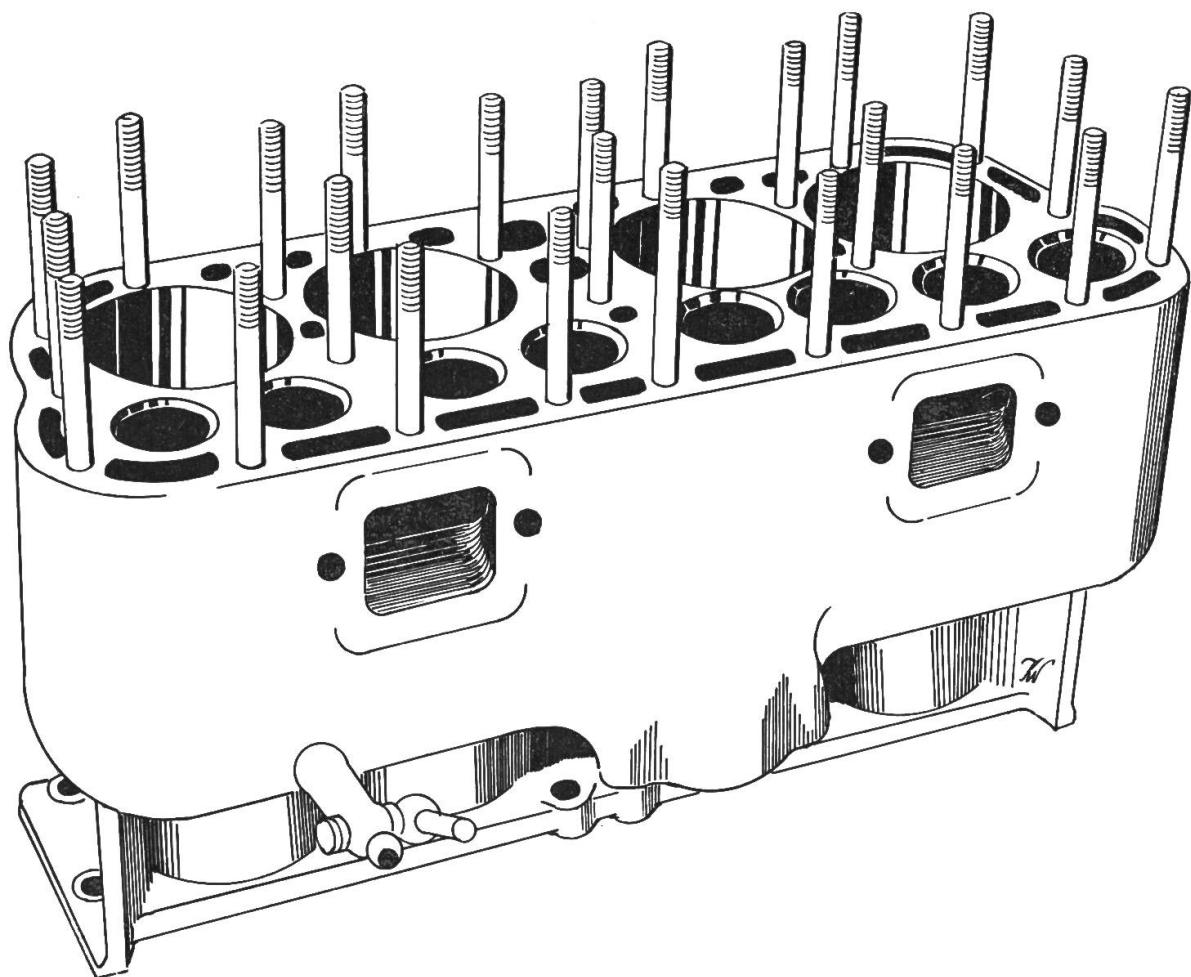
Zylinderblock eines älteren 4-zylindrigen Benzinmotors. Die vielen Schraubenbolzen sind nötig, damit eine einwandfreie Abdichtung der einzelnen Verbrennungsräume möglich ist. Heute wird dieser Teil meist mit dem Kurbelgehäuseoberteil zusammengegossen.
